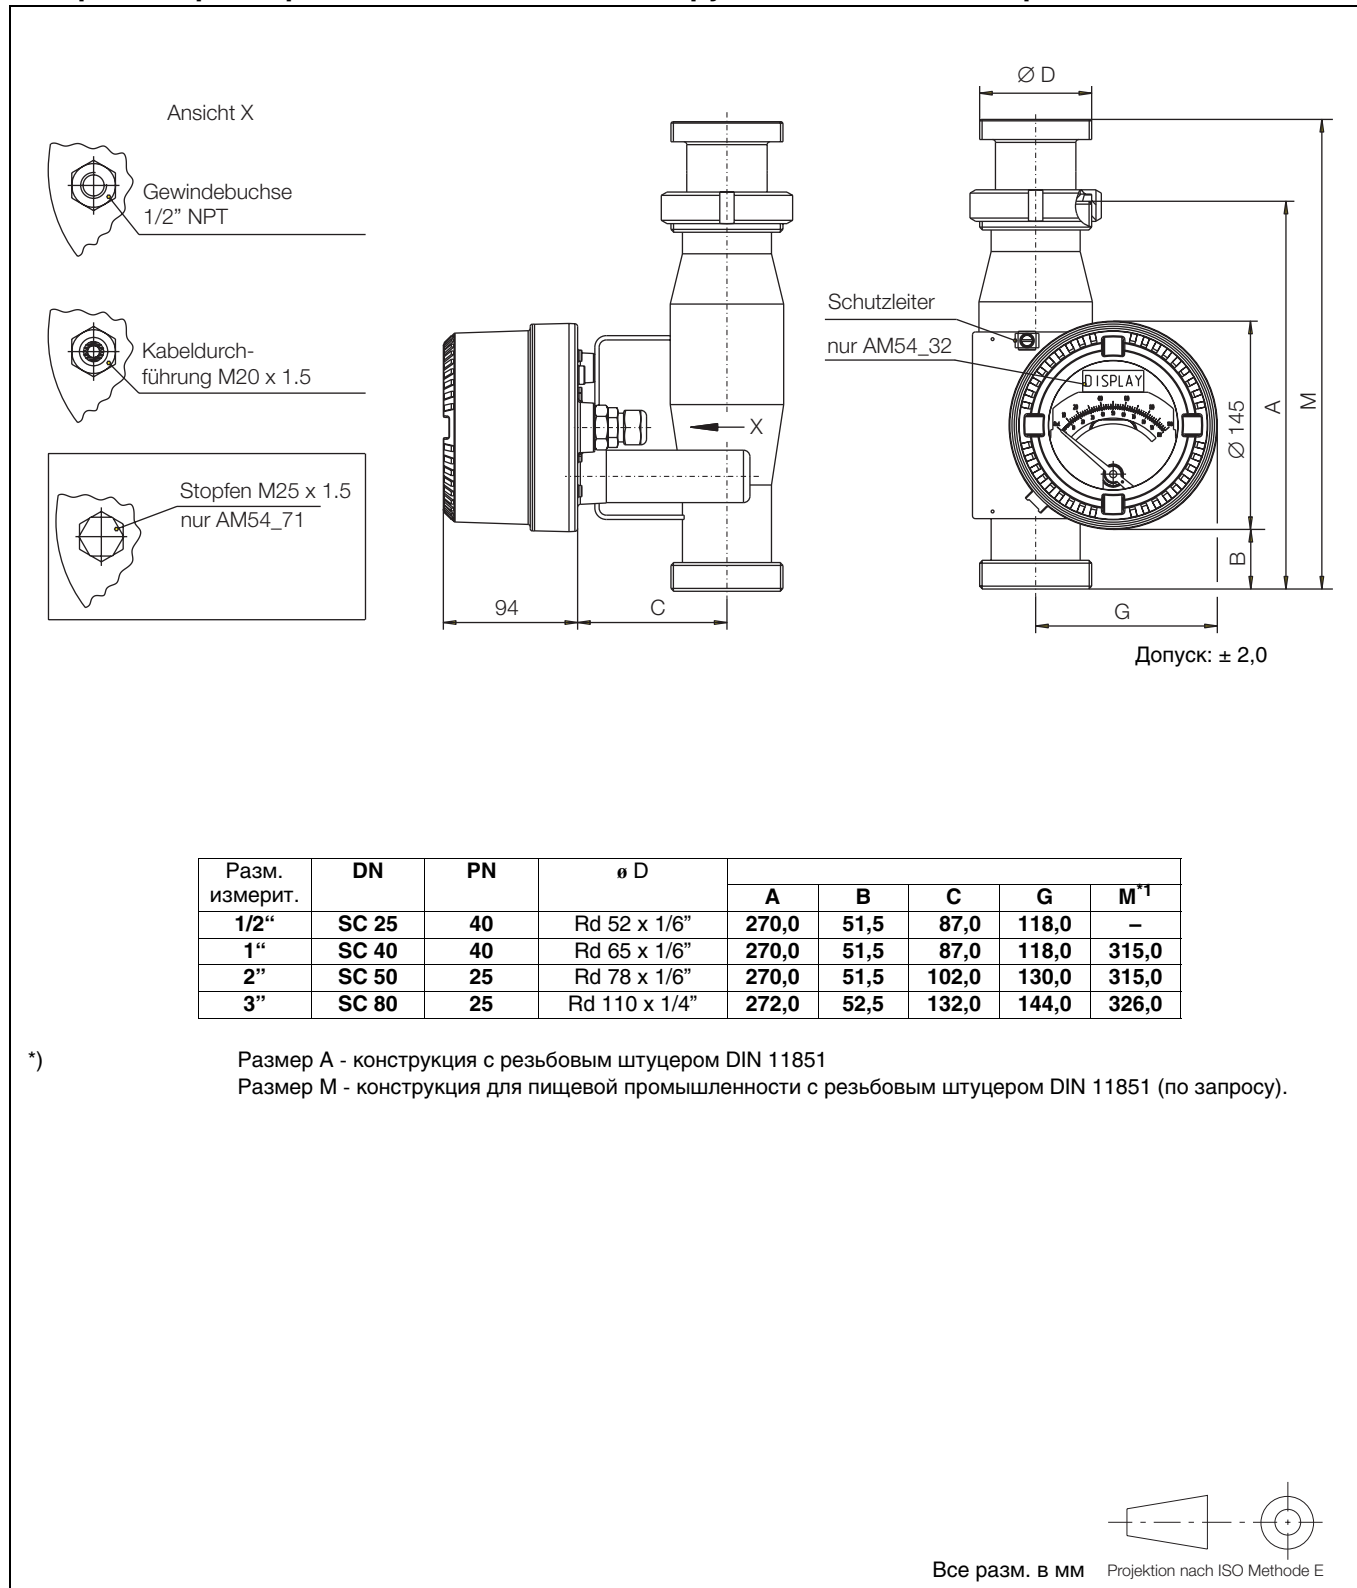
Габаритные размеры и соединения для пищевой промышленности.
